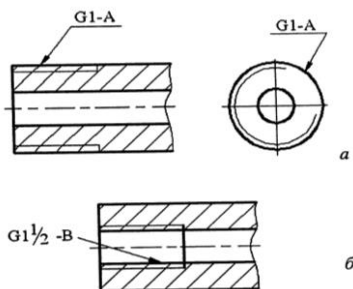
Обозначение трубной цилиндрической резьбы:
